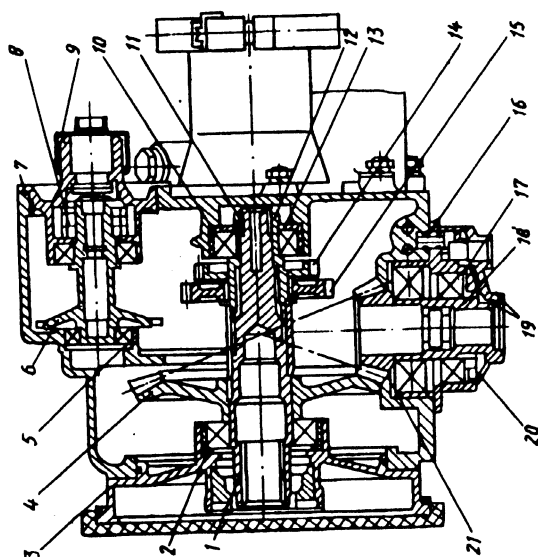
Коробка приводов (вертикальный разрез по оси двигателя);
